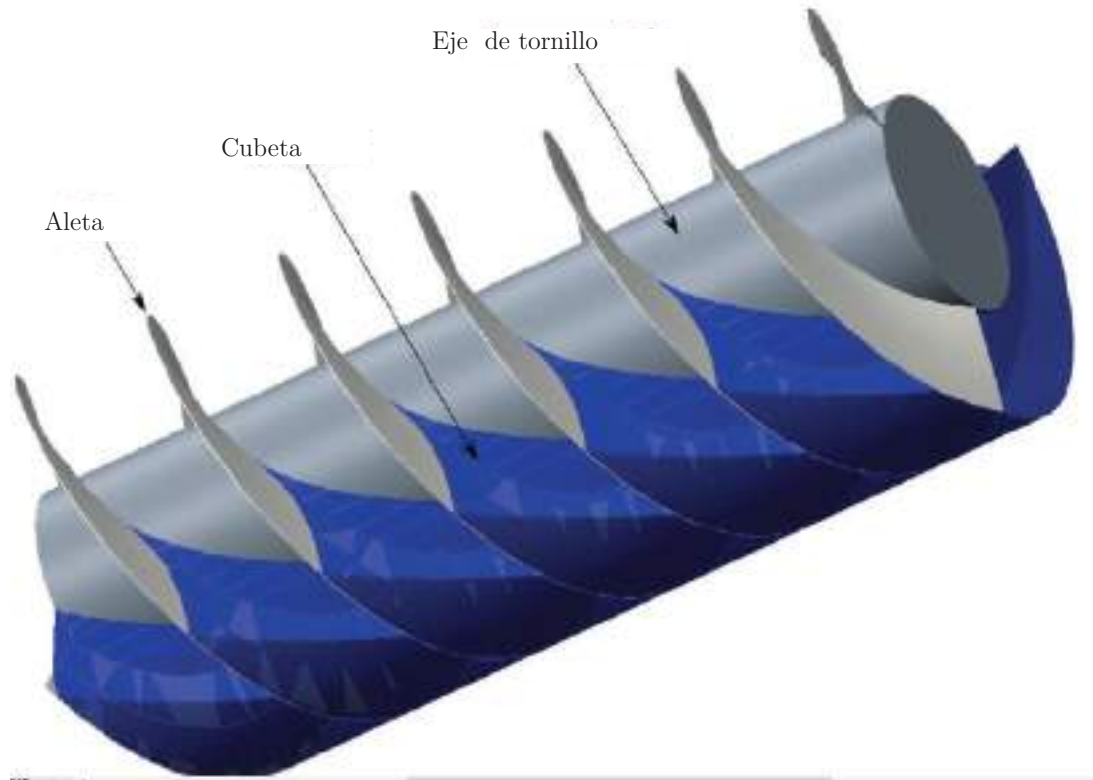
Esquema de tornillo en el punto de llenado óptimo con los distintos "baldes" de agua. Fuente: [31]
